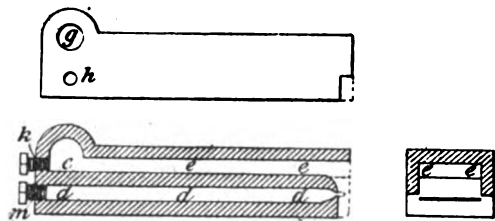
, 5 et 6. — Élévation, coupe longitudinale et coupe transversale en bout du brûleur.
